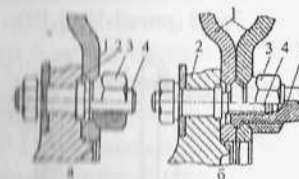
Способы крепления дисковых колес грузовых автомобилей: а – крепление переднего (одинарного) колеса; б – крепление задних (сдвоенных) колес; 1 – диск; 2 – ступица; 3 – гайка; 4 – шпилька; 5 – колпачковая гайка (футорка)
